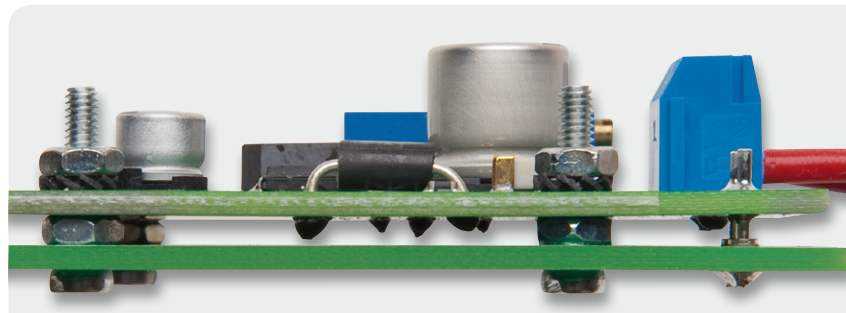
Die Befestigung des SDW 35 mit Kontermuttern
